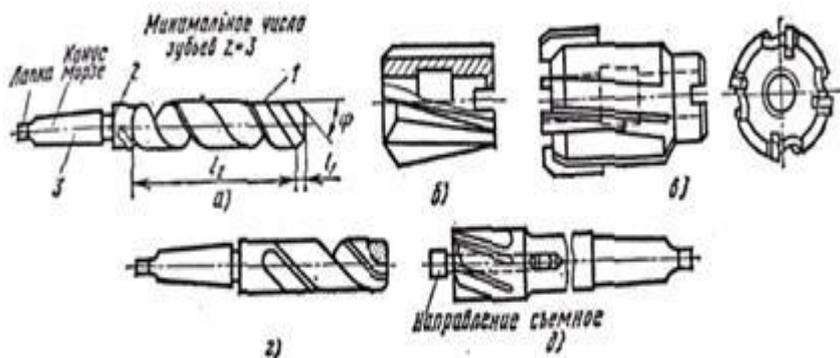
Зенкеры: а—цельный с коническим хвостовиком, б—насадной цельный, в—насадной с наборными ножками, г—оснащенный твердосплавной пластинкой, д—с направлением для цилиндрических углублений
